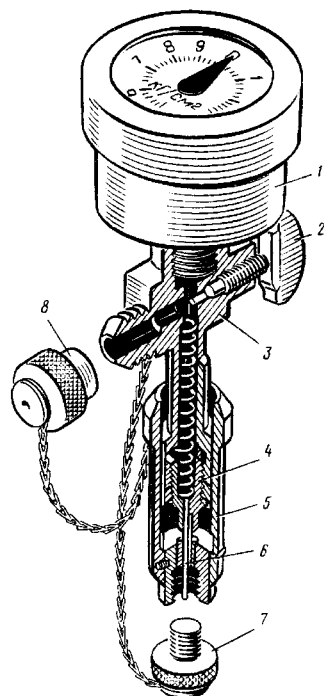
Приспособление для проверки давления и зарядки пневматиков колес:
